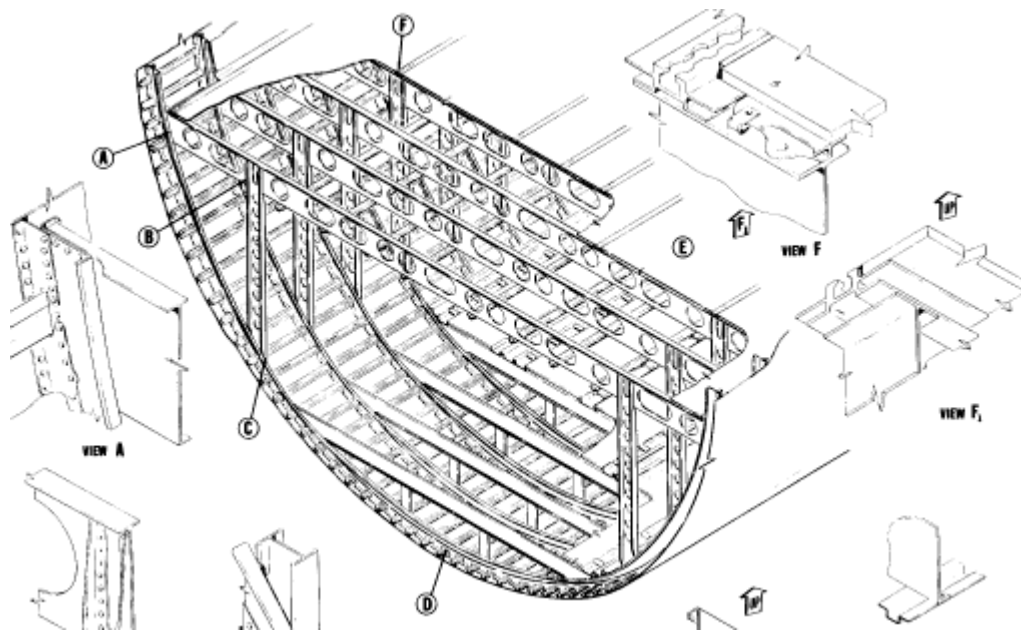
Painéis e estruturas de cavernas e vigas omega (STANFORD, 2009).
